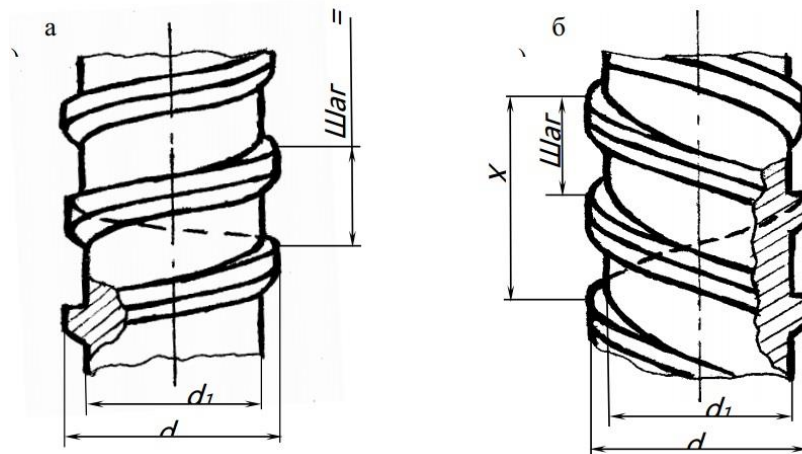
Шаг резьбы однозаходной и многозаходной резьбы
